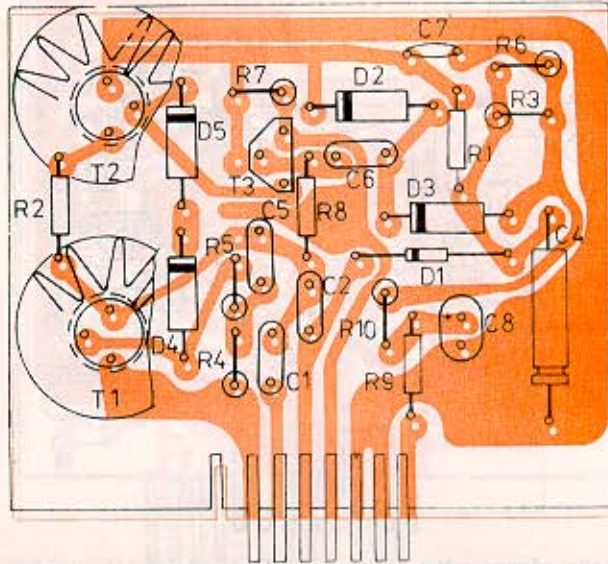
Deska záznamového zesilovače (pohled ze strany součástek)
